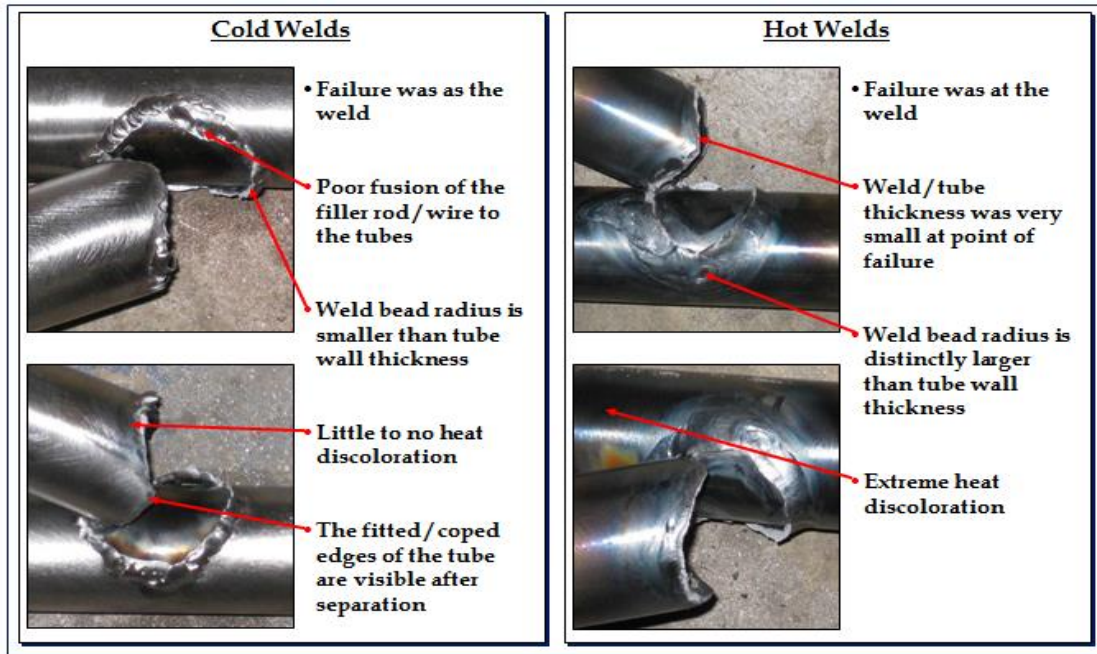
Pruebas destructivas de soldadura no válidas [8]
